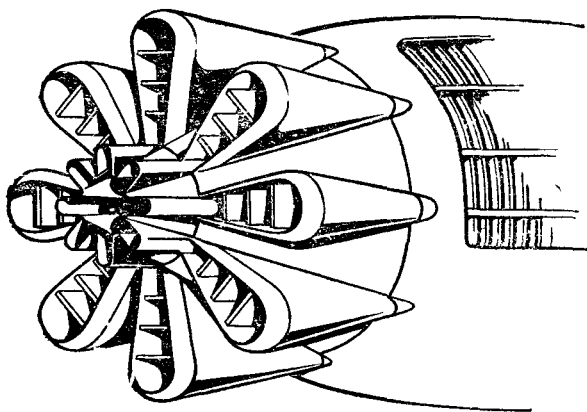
Восьмилепестковый глушитель реактивного двигателя.
